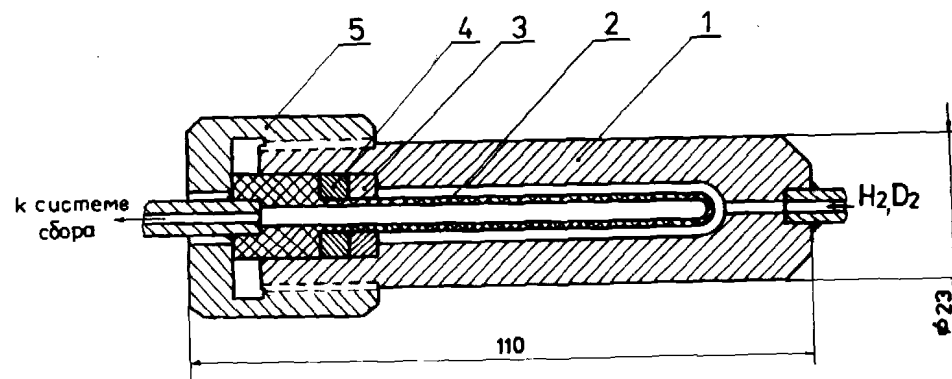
Измерительная ячейка. 1 - корпус, 2 - образец, 3 - упорное кольцо, 4 - медная прокладка, 5 - накидная гайка.
